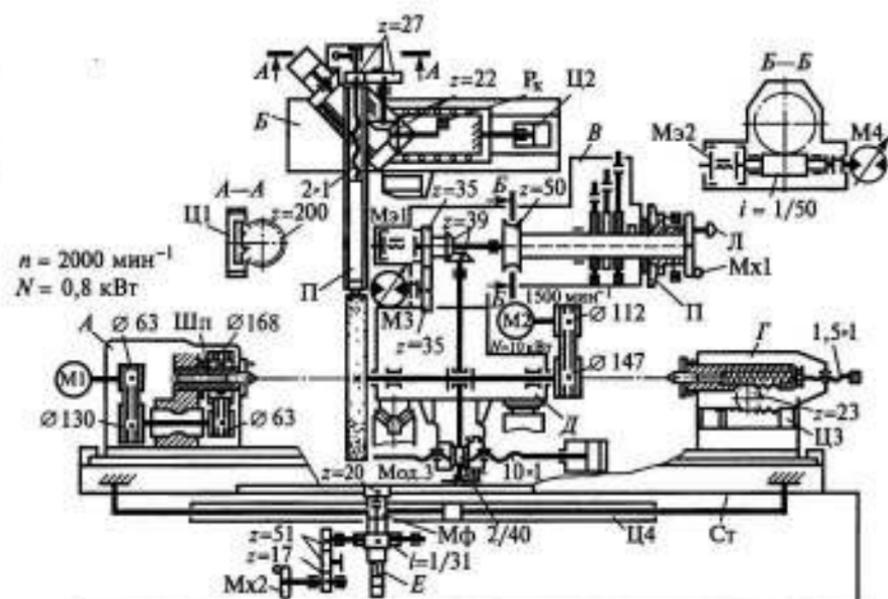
Кинематическая схема центрального круглошлифовального станка:
